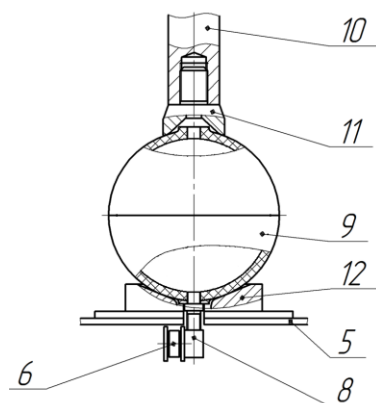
Схема ультразвуковой сварки изделий в устройстве конвейерного типа
